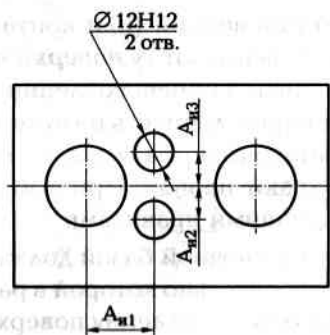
Эскиз обрабатываемой детали к заданию 1.29
